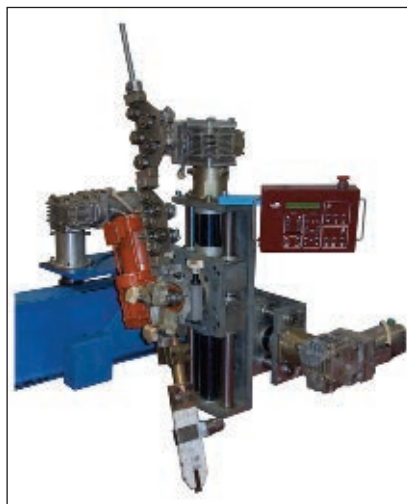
Установка КТС 4-1 для наплавки плоских поверхностей
